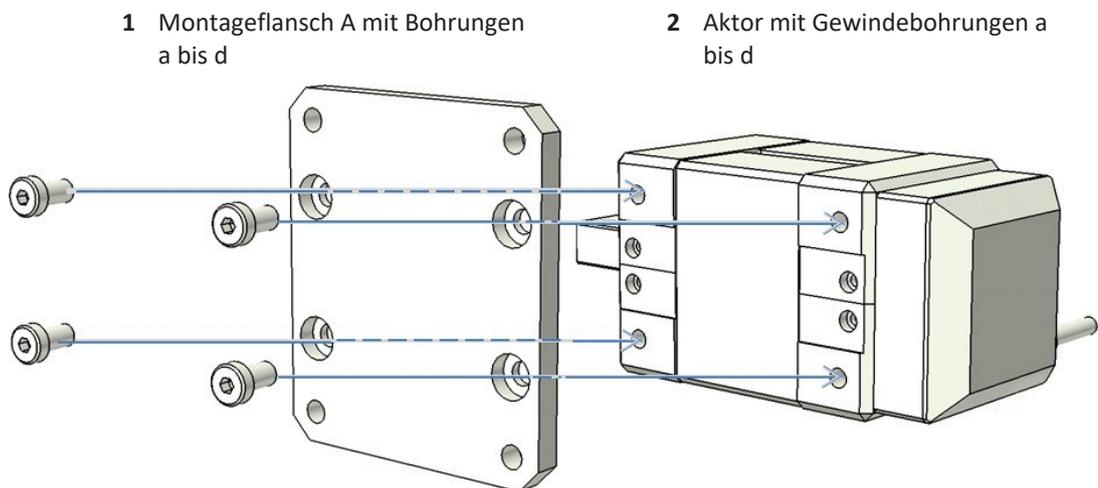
Montage des Montageflanschs A (Explosionsdarstellung)
